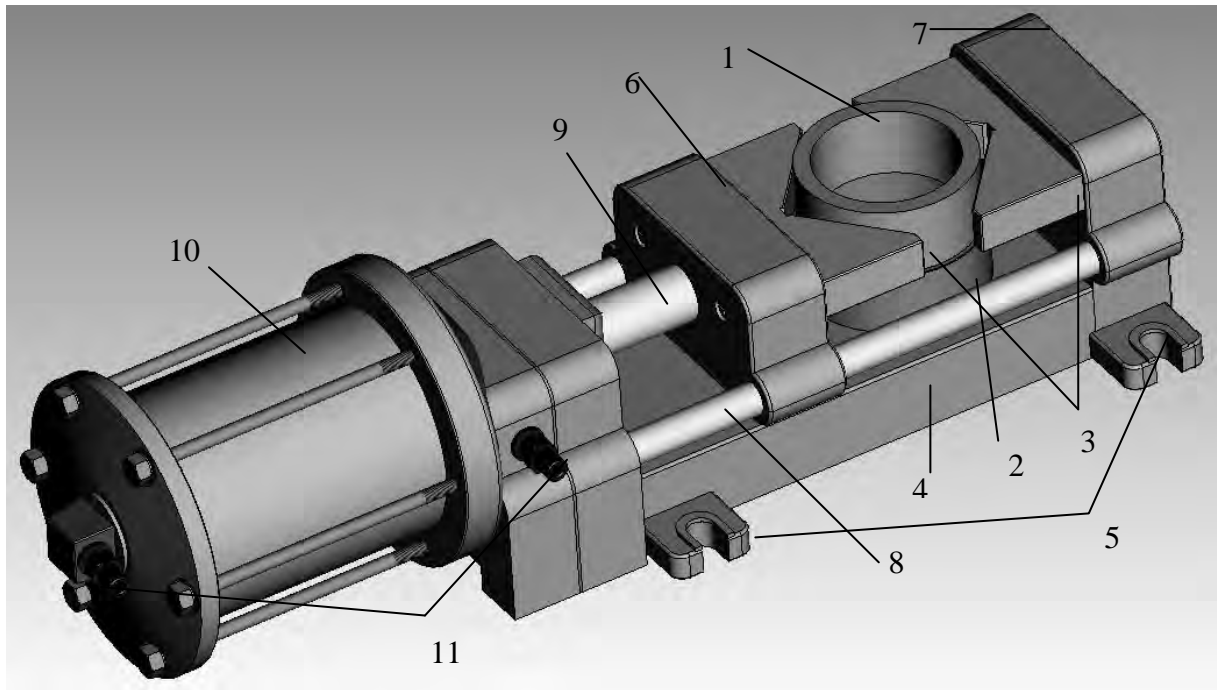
Пристрій для оброблення внутрішньої поверхні кільця підшипника ковзання
